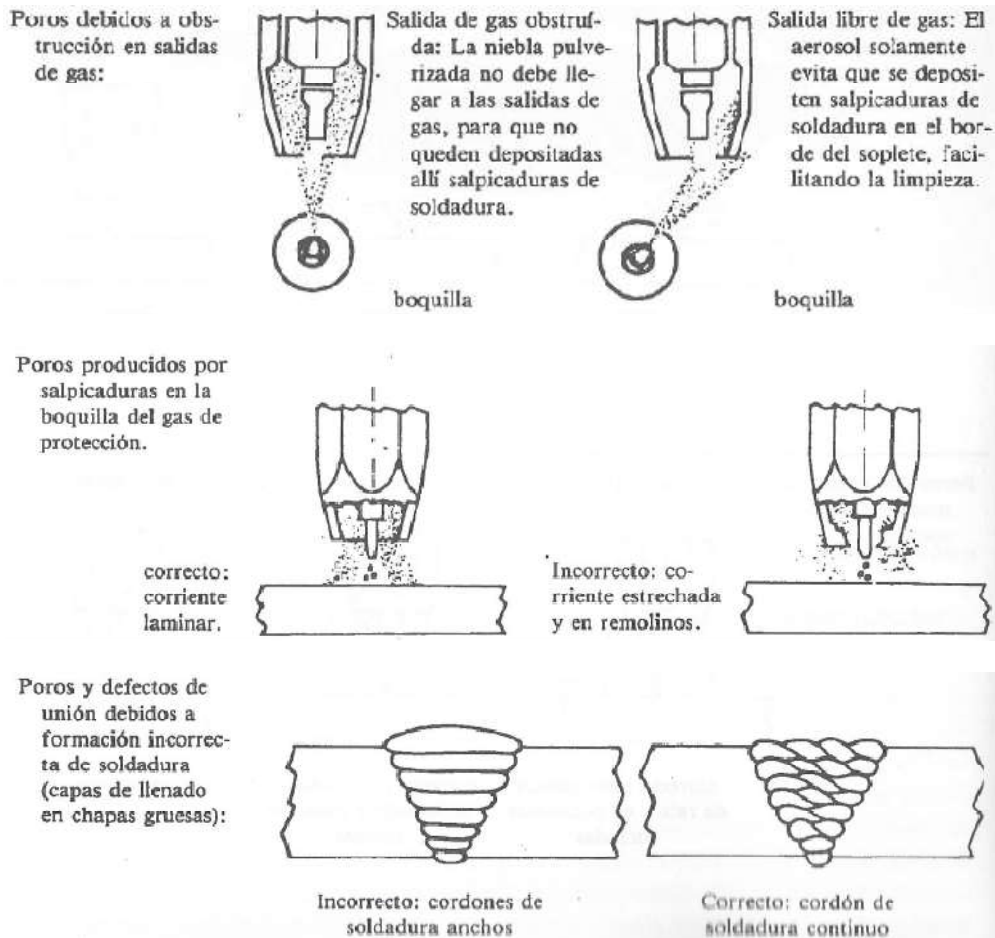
Defectos y causas en la operatoria de la soldadura GMAW. [11]
